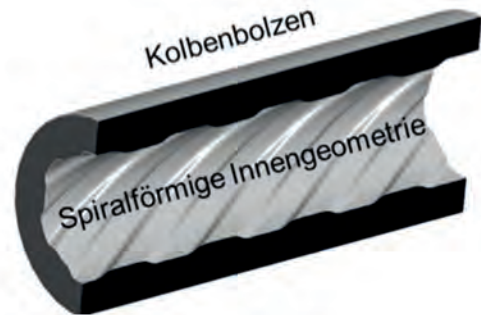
Kolbenbolzen mit spiralförmiger Innengeometrie [2]
